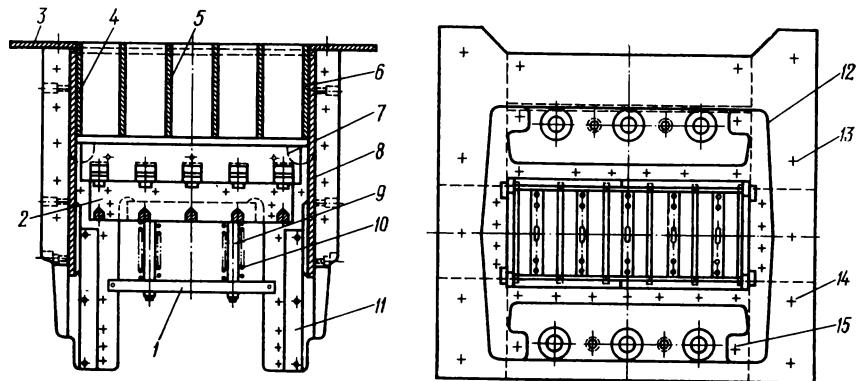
Формовочный ящик пресса-автомата РА-550:
